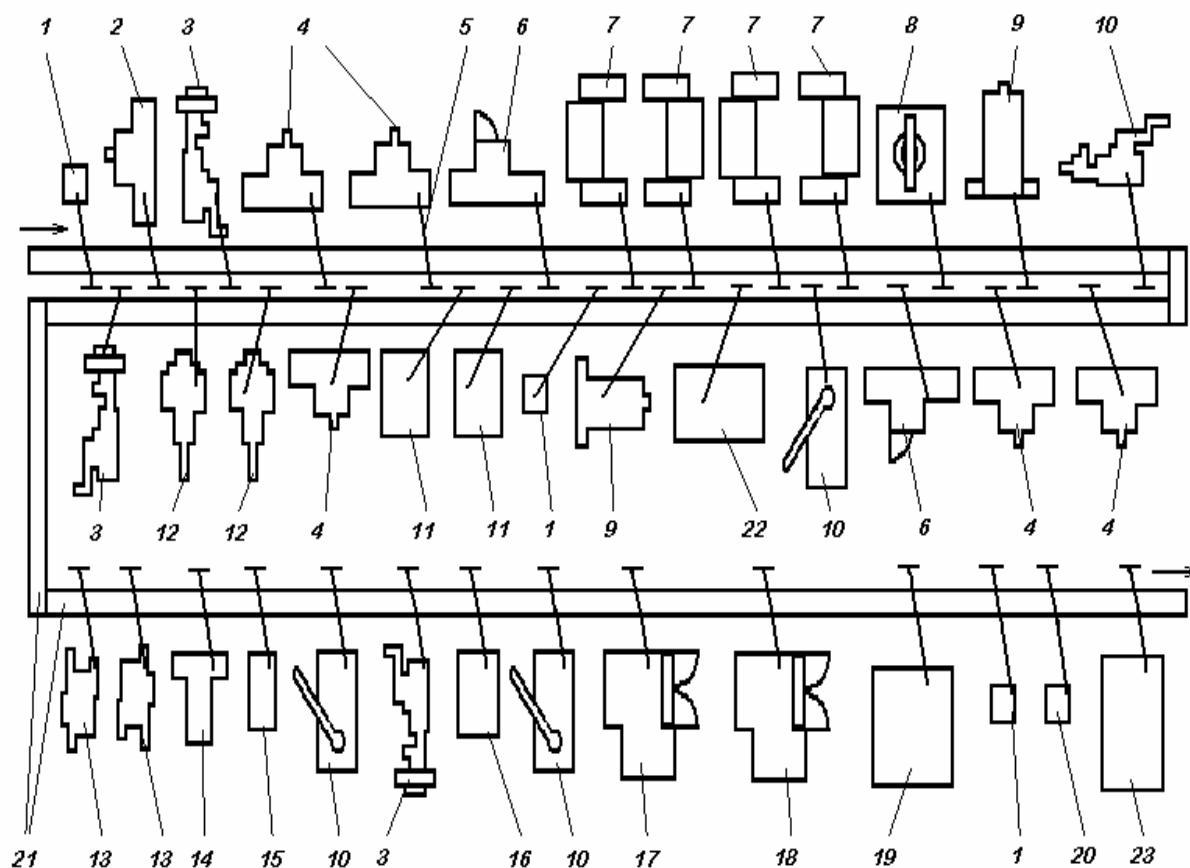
Пример планировки ПМЛ восстановления коленчатых валов двигателей КамаЗ-53212: 1 – магнитный дефектоскоп МД-50П; 2 – пресс гидравлический П-6326; 3 – станок токарно-винторезный 16К20; 4 – станок круглошлифовальный ЗМ152; 5 – подъемник пневматический 12402; 6 – станок круглошлифовальный ЗВ423; 7 – станок наплавочный У-653М; 8 – печь электрическая шахтная СНОЛ 1,8.1,6.3,0/1000; 9 – пресс гидравлический П-6330; 10 – станок радиально-сверлильный 2М53; 11 – полуавтомат торцешлифовальный ЗТ161Е; 12 – станок горизонтально-фрезерный 6Р83Г; 13 – полуавтомат круглошлифовальный ХШ2-12Н; 14 – полуавтомат круглошлифовальный ХШ2-01; 15 – стенд сборочный 70-7362-1518; 16 – станок балансировочный КИ-4274; 17 – полуавтомат суперфинишный 3875К; 18 – полуавтомат полировальный 3835К; 19 – установка для очистки ОМ-3600; 20 – верстак слесарный ОРГ 5365; 21 – конвейер роликовый 12398; 22 – высокочастотный генератор ВЧГ-100/0,66УЧ; 23 – ванна консервации 04.04.084.00.000
